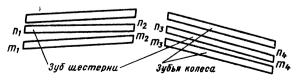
Схема расположения зубьев шестерии и колеса при центровании
